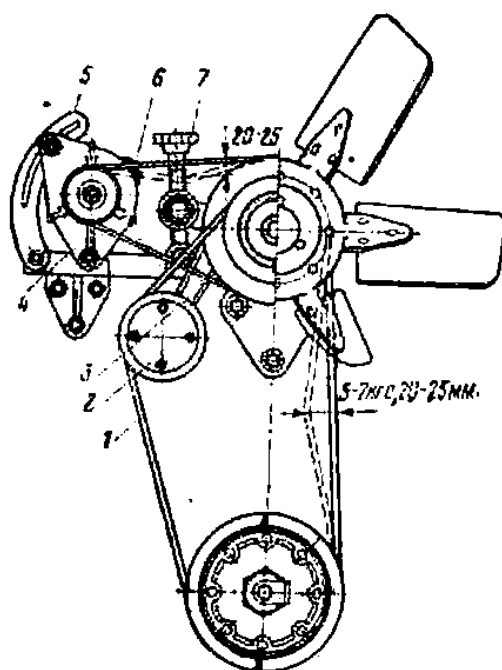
Устройство для натяжения ремней привода вентилятора и генератора двигателя Д-130Т
